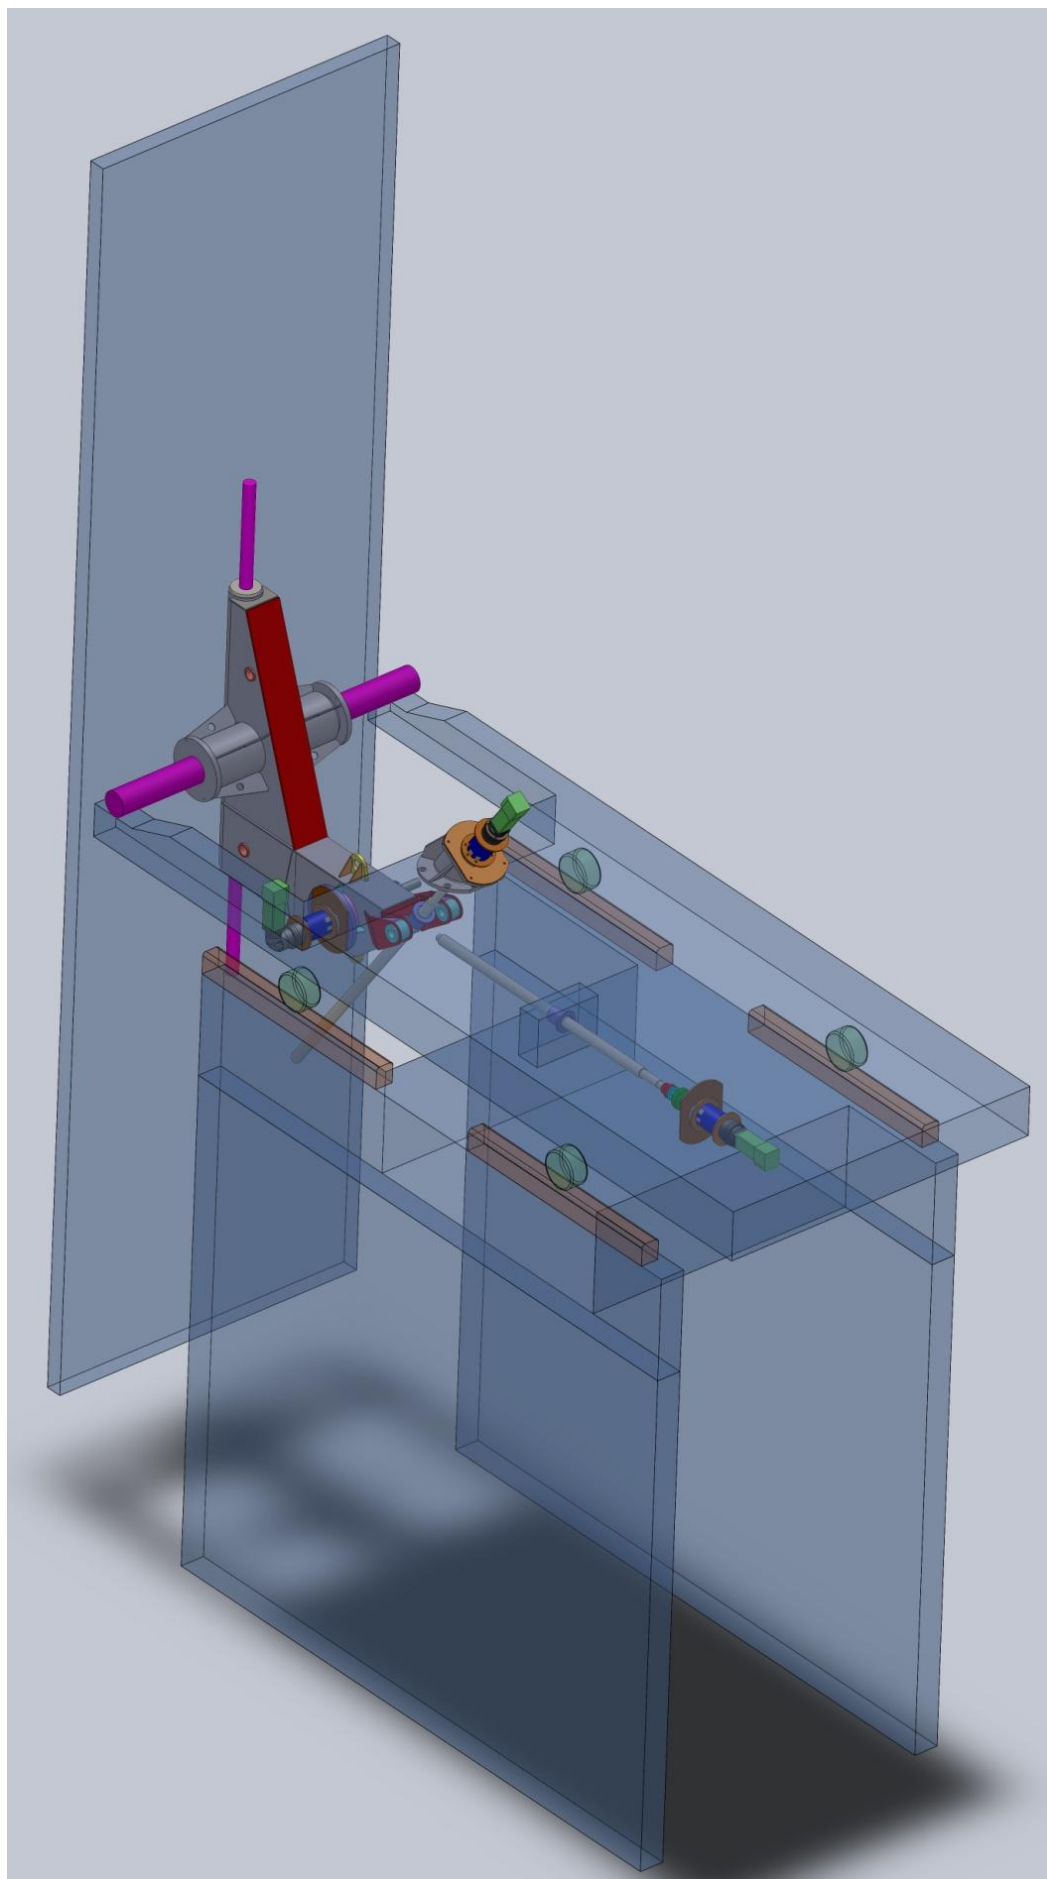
Щит РАТАН-600 с новыми приводами, вид 3D
